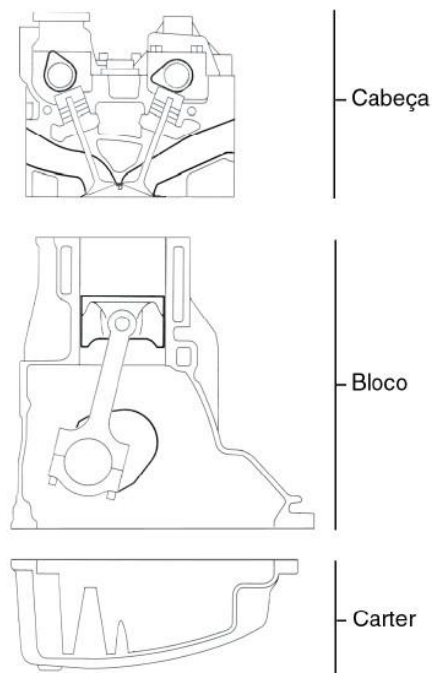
Três grandes componentes de um motor a combustão interna [8].
